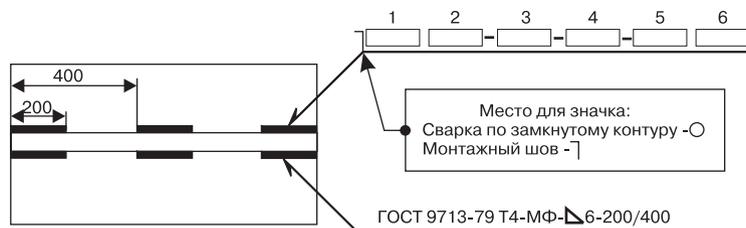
Обозначение сварных швов на чертежах по ГОСТ 2.312-72\
